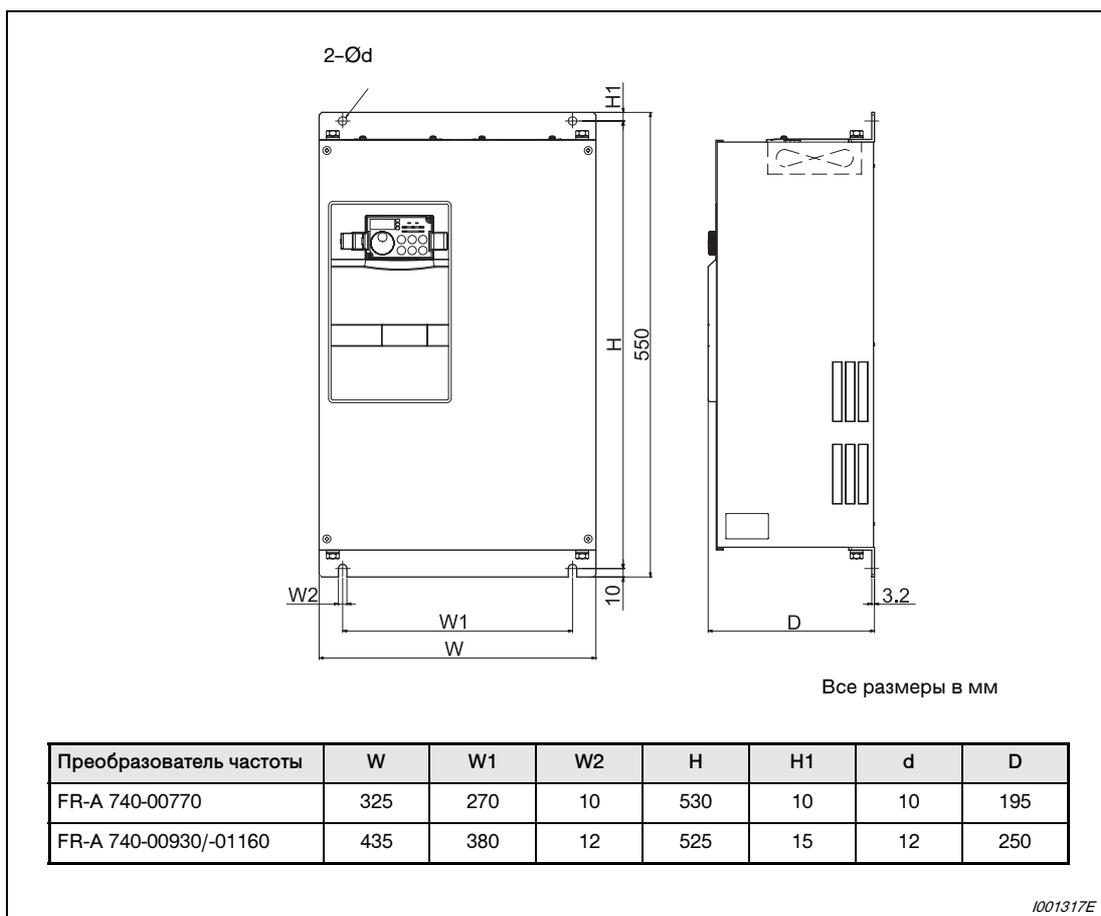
Размеры FR-A 740-00770 ... -01160
